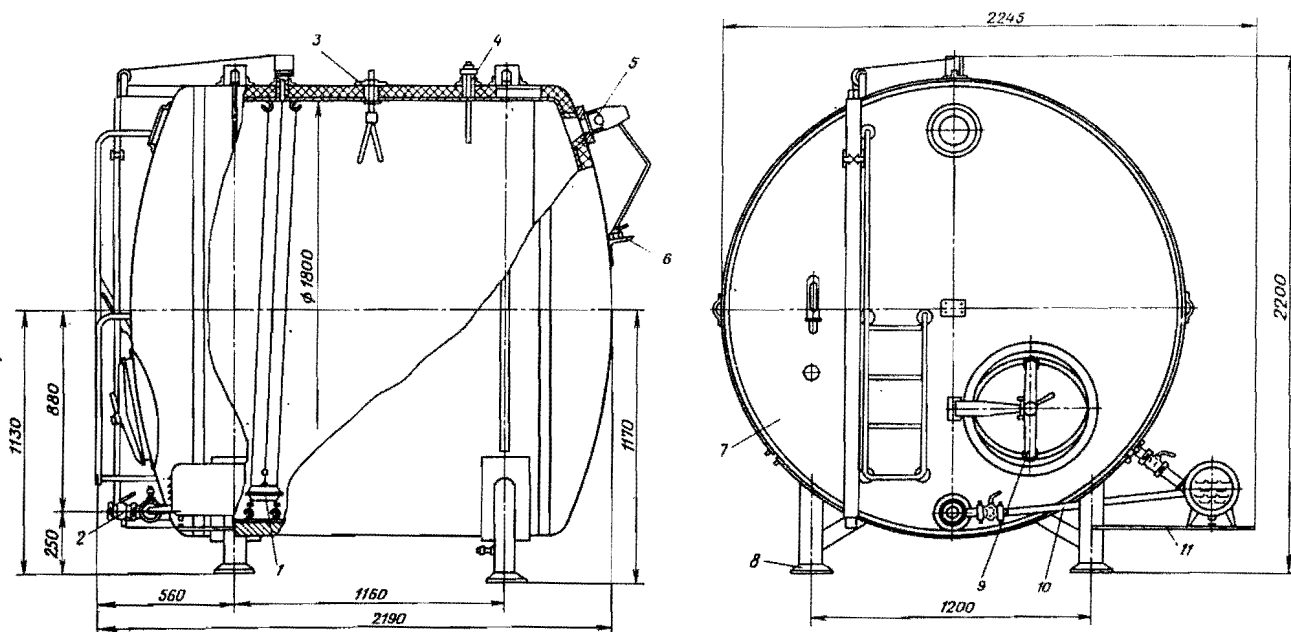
Общий вид резервуара марки В2-ОМГ-4,0:
